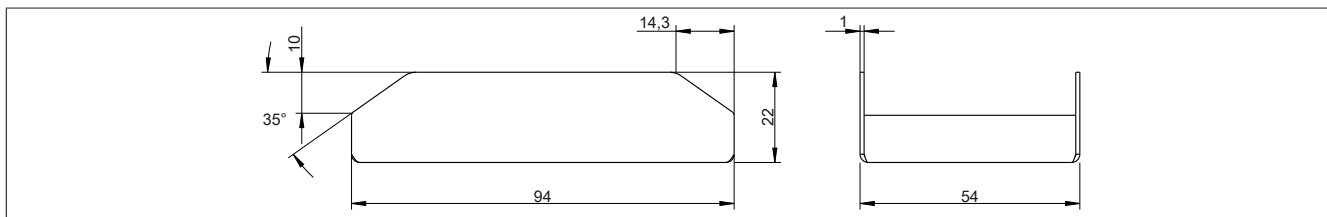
5AC804.MFLT-00 - Abmessungen
